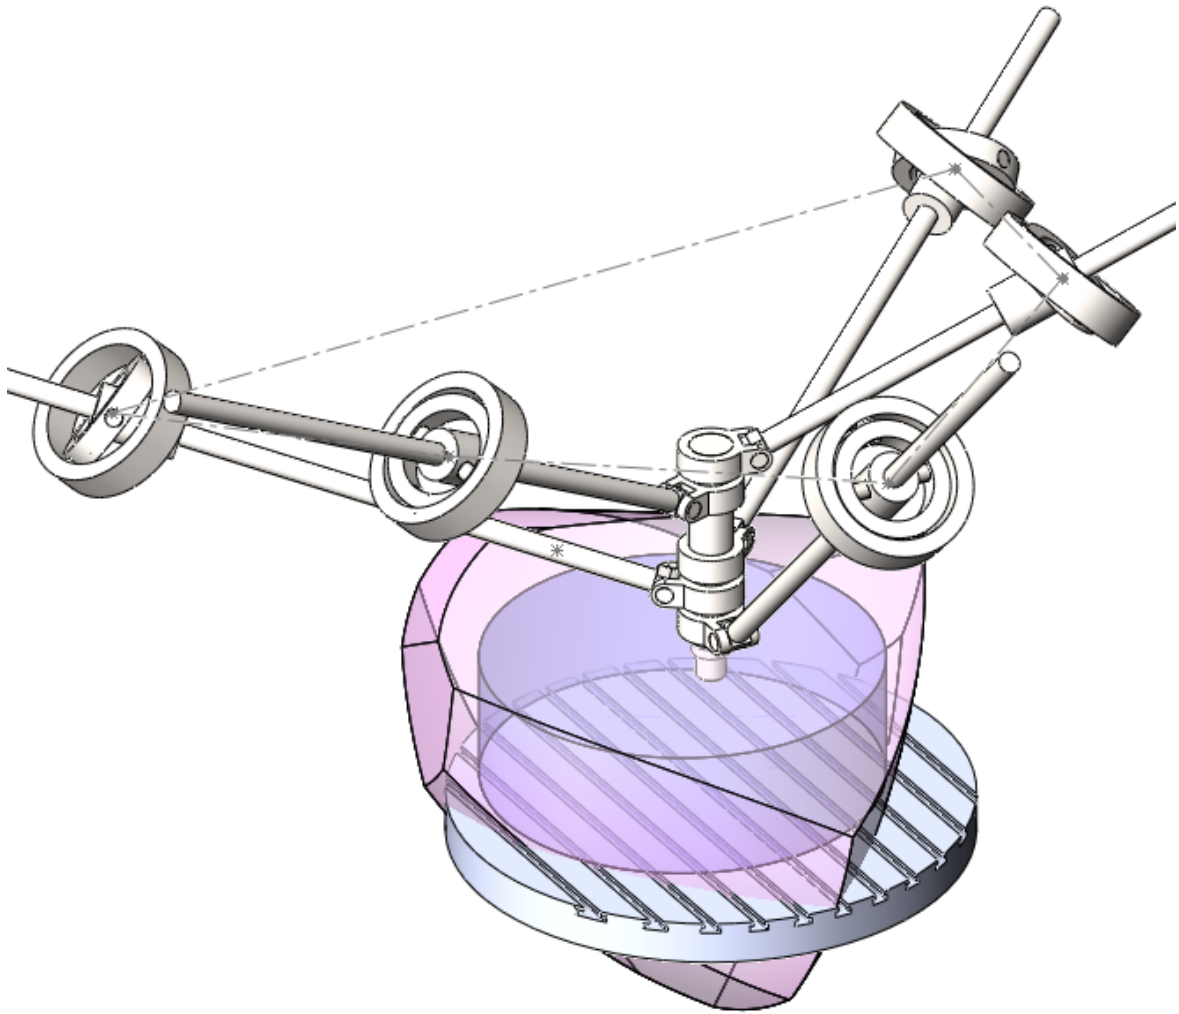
Максимальні габарити заготовки при верхньому положенні столу
